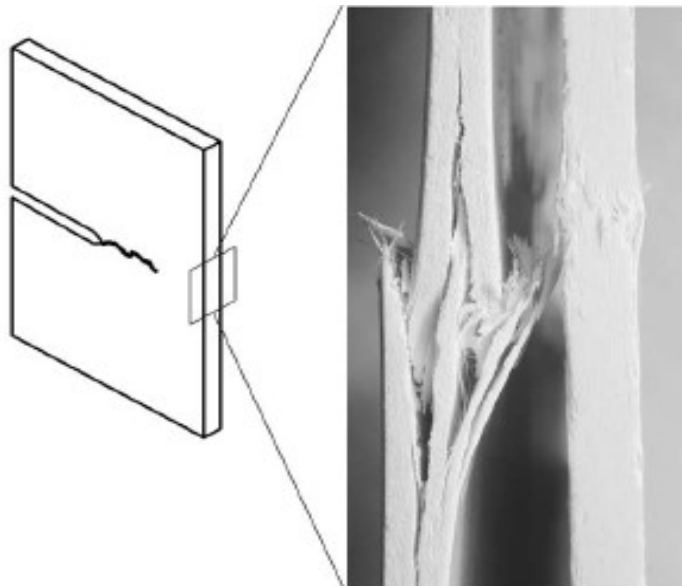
Endommagement par compression du bord arrière de l'éprouvette (CT) [85]
